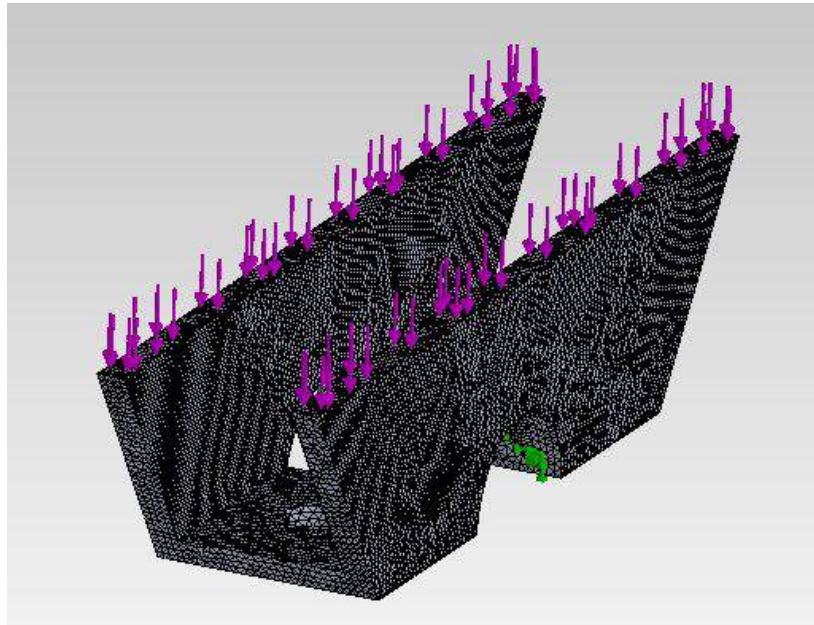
Mallado pieza sujeción eje horizontal cargas hacia abajo.
